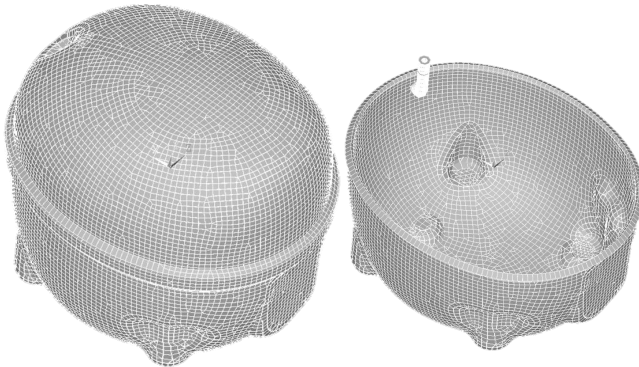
Malha da carcaça em elementos de placa juntamente com a malha do passador em elementos de viga.
